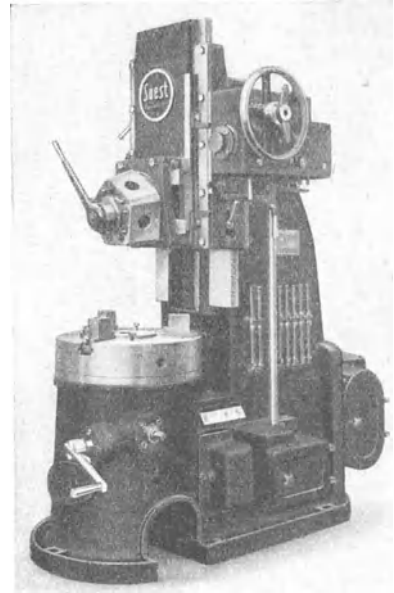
Senkrechtbohrmaschine mit Revolverkopf. (Louis Soest & Co. G. m. b. H., Düsseldorf-Reisholz.)
